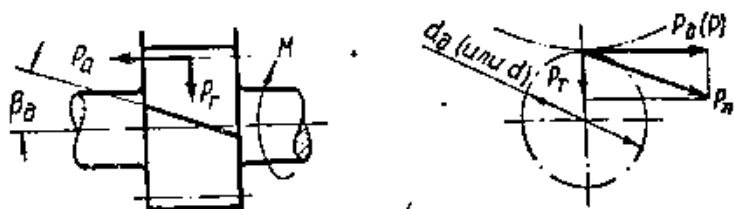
Схема усилий в зацеплении цилиндрических зубчатых колес.
